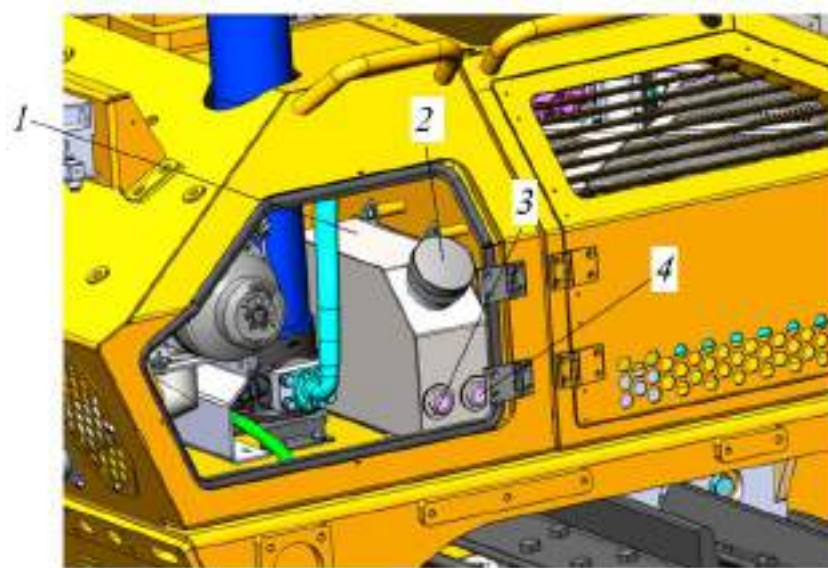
Заправка масла в систему смазки уплотнения редуктора
